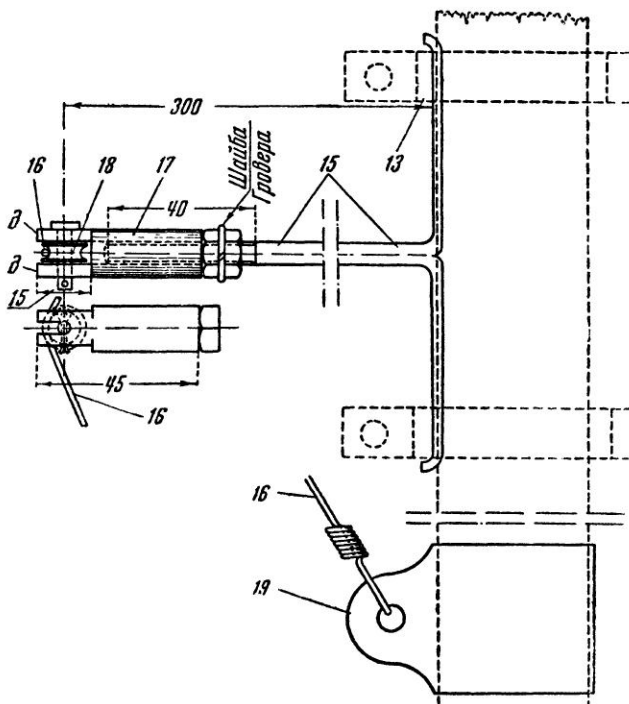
Устройство стержня переднего вылета с натяжной насадкой:
